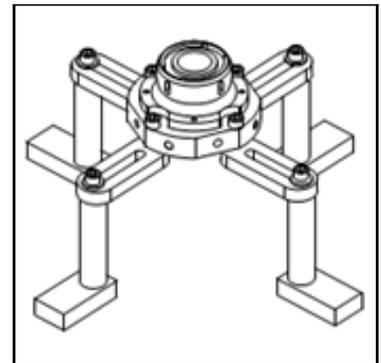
MONTAJE RODAMIENTO ESFÉRICO UNIVERSAL
